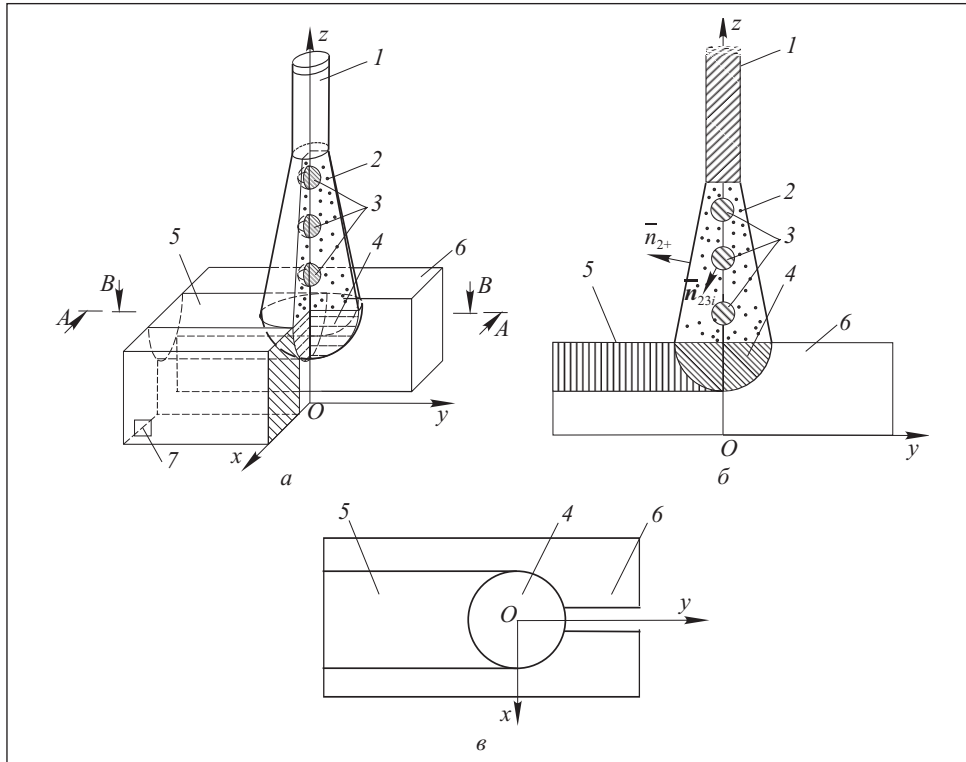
Схема дуговой сварки: а — общий вид; б — разрез по сечению AA; в — разрез по сечению BB; 1 — электрод; 2 — дуга; 3 — капли расплавленной части электрода; 4 — ванна с расплавом; 5 — сварной шов; 6 — свариваемые детали; 7 — контакт
